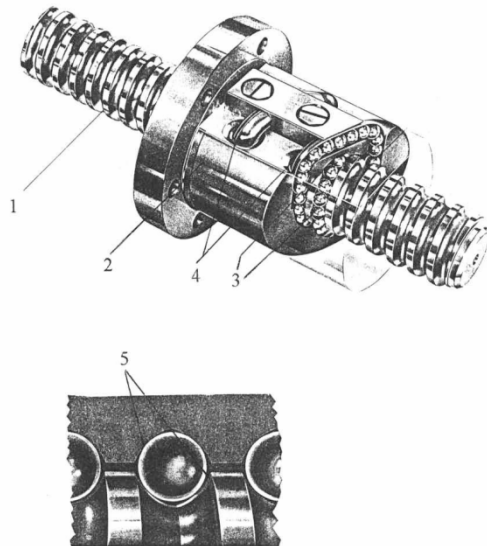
Конструктивное исполнение шариковой винтовой пары с вращающимся винтом и перемещающейся гайкой:
